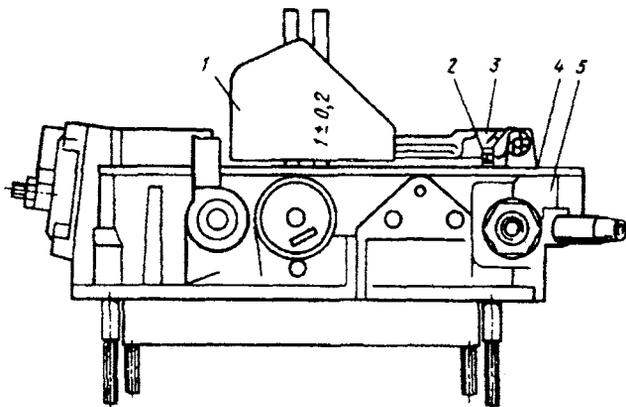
Установка уровня топлива в поплавковой камере:
